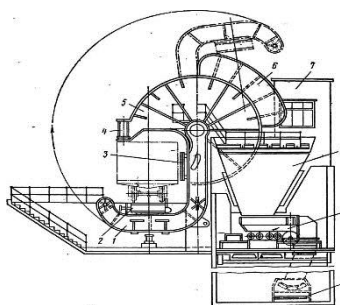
Стационарный боковой вагоноопрокидыватель.
